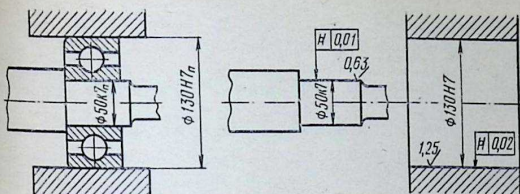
Обозначение посадок подшипников качения на чертежах.
